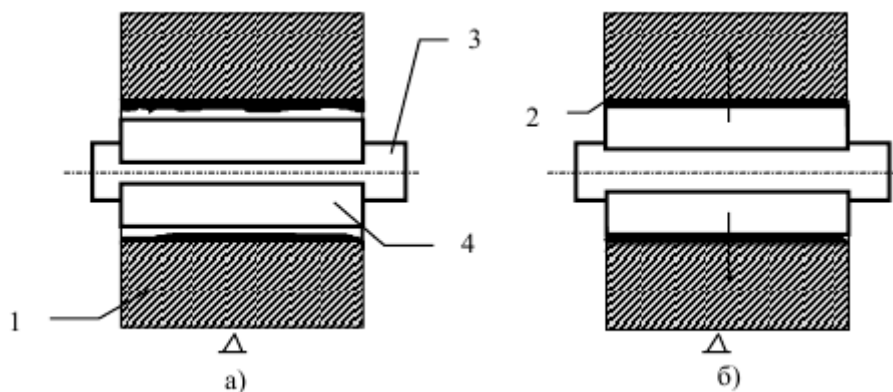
Схема формування полімерної композиції на поверхні зношеного отвору корпусної деталі: а) оправка з кільцями в стислуому стані; б) калібрування полімерної композиції стисливими кільцями; 1 - корпус; 2 - шар полімеру; 3 - оправка; 4 - півкільця.
